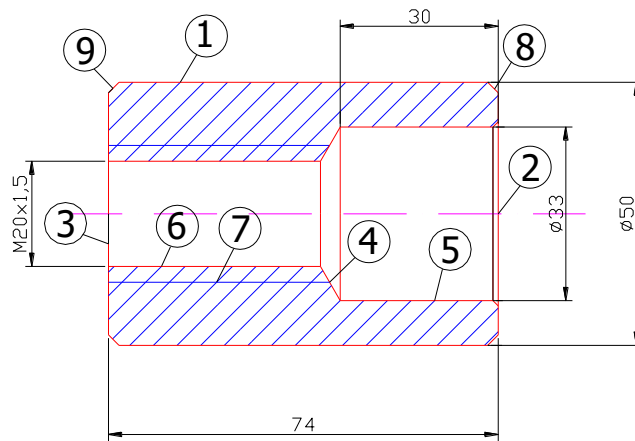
Ескіз деталі представника та оброблювані поверхні
